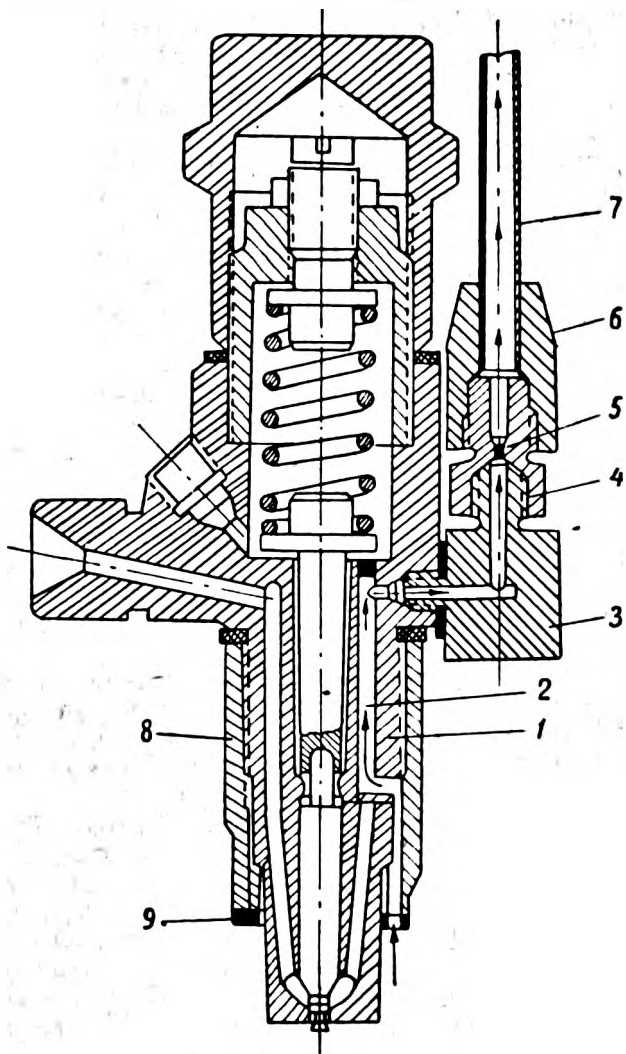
Форсунка для отбора давления газов из цилиндра двигателя.
